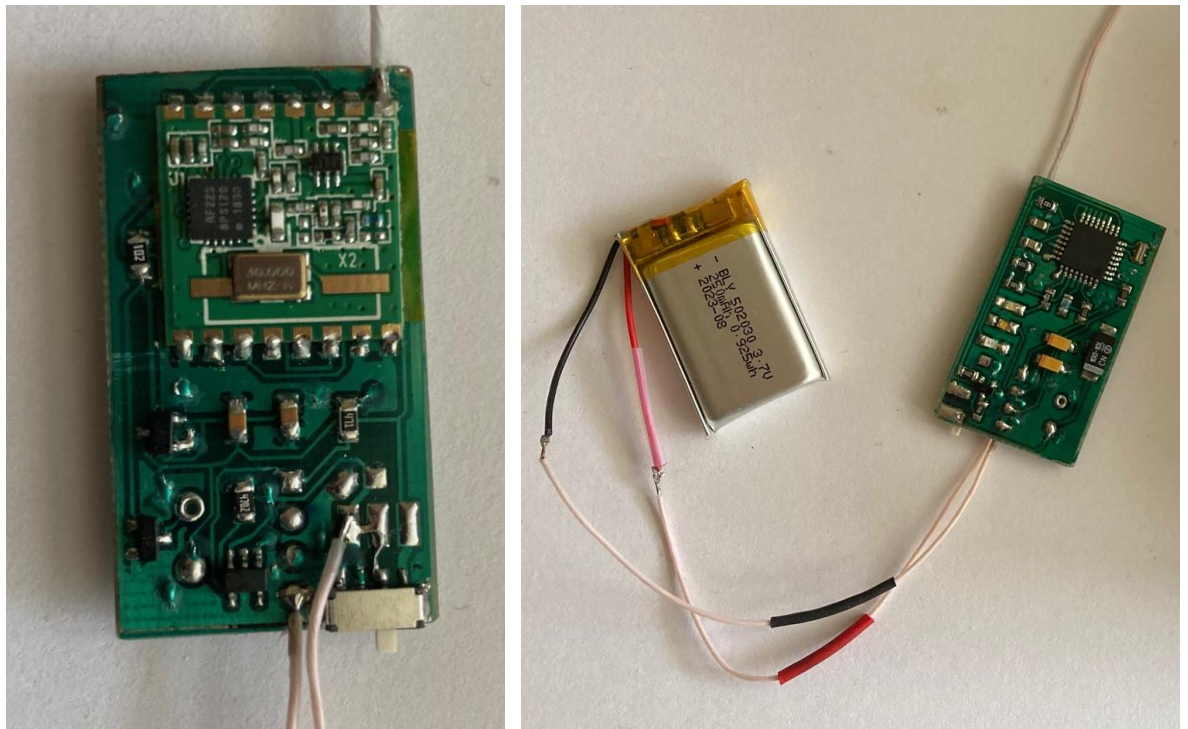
Загальний вигляд прототипу пошукового маяка
